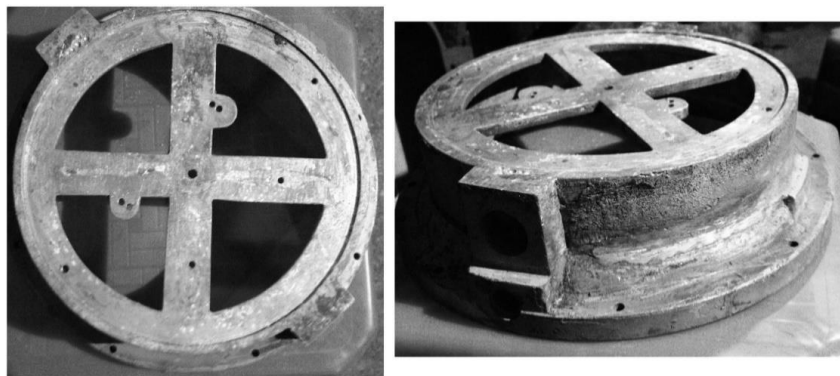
Вид внутренней несущей конструкции Репитера
